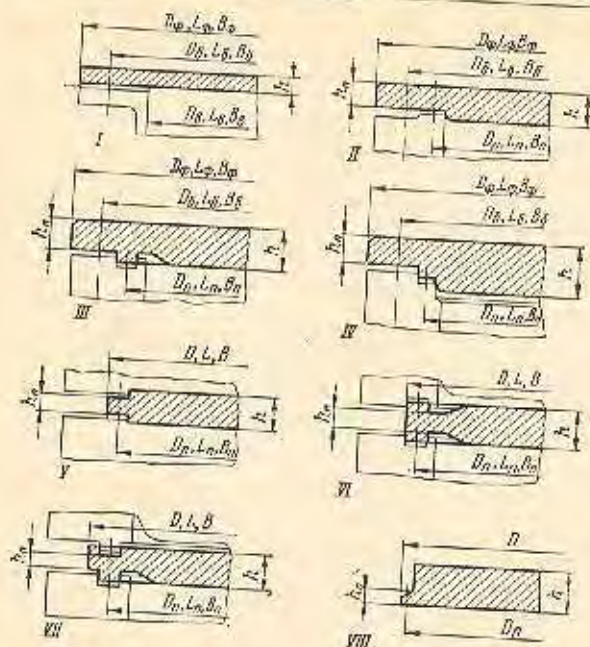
Основные типовые конструкции плоских фланцевых крышек: I-IV — цельные круглые и прямоугольные фланцевые крышки; V-VII — вкладыши между фланцами круглых и прямоугольных крышек (заглушки); VIII — вкладыши круглых крышек для аппаратов высокого давления
